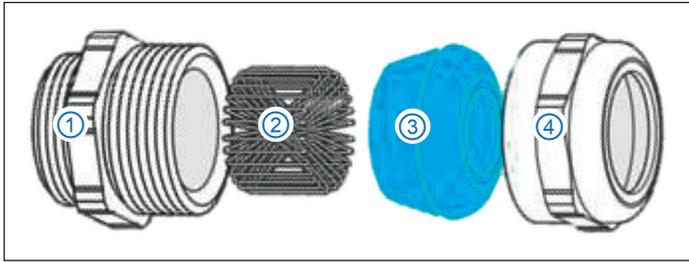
Komponenten einer Kabelverschraubung mit Kontaktierung des Schirms
